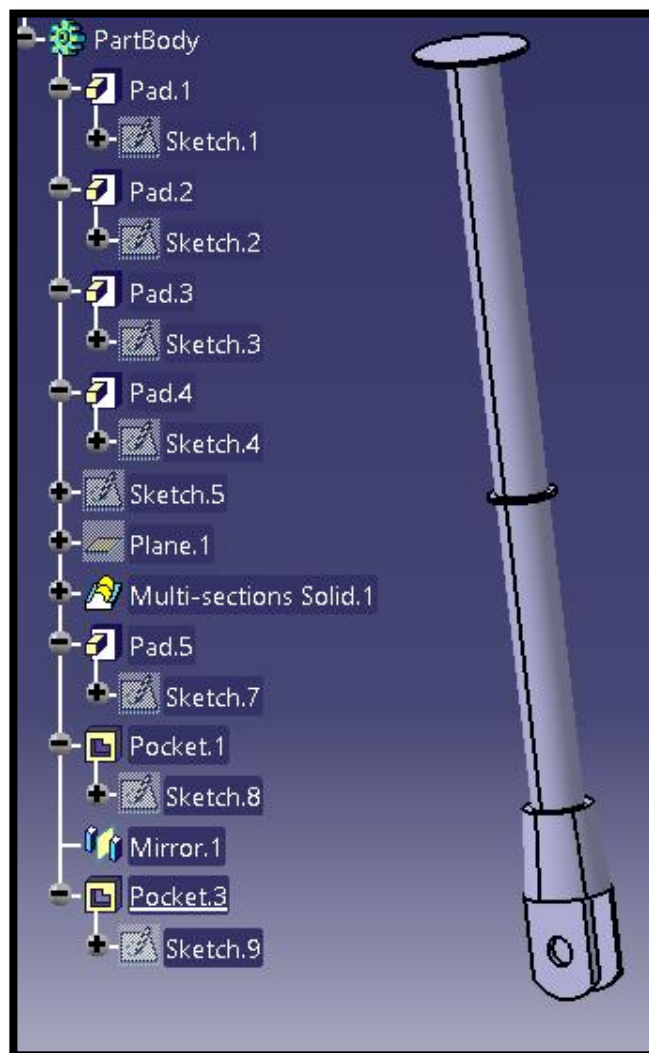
Seat mounting frame 11: Pieza 2 amortiguador + árbol de operaciones
